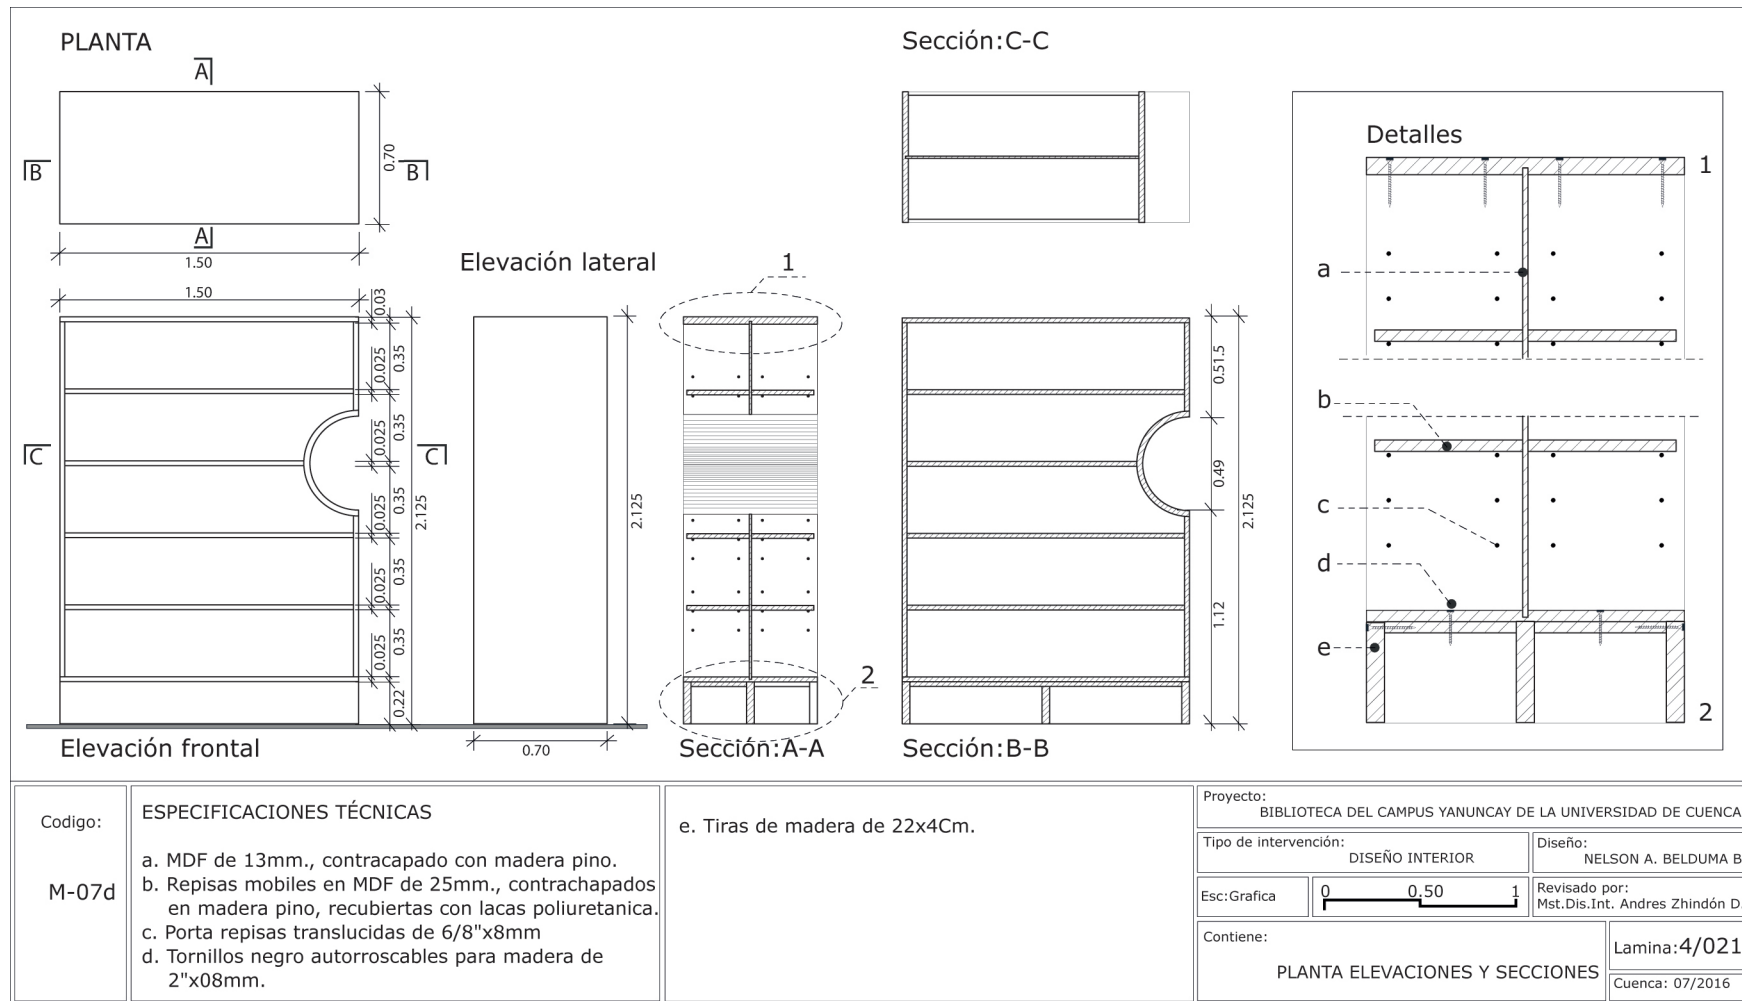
Planta, elevaciones y secciones. Estanterías. M-07d.
